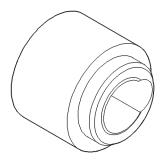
Ferramenta de Vedação e Alinhamento da Tampa da Caixa de Regulagem 6139
